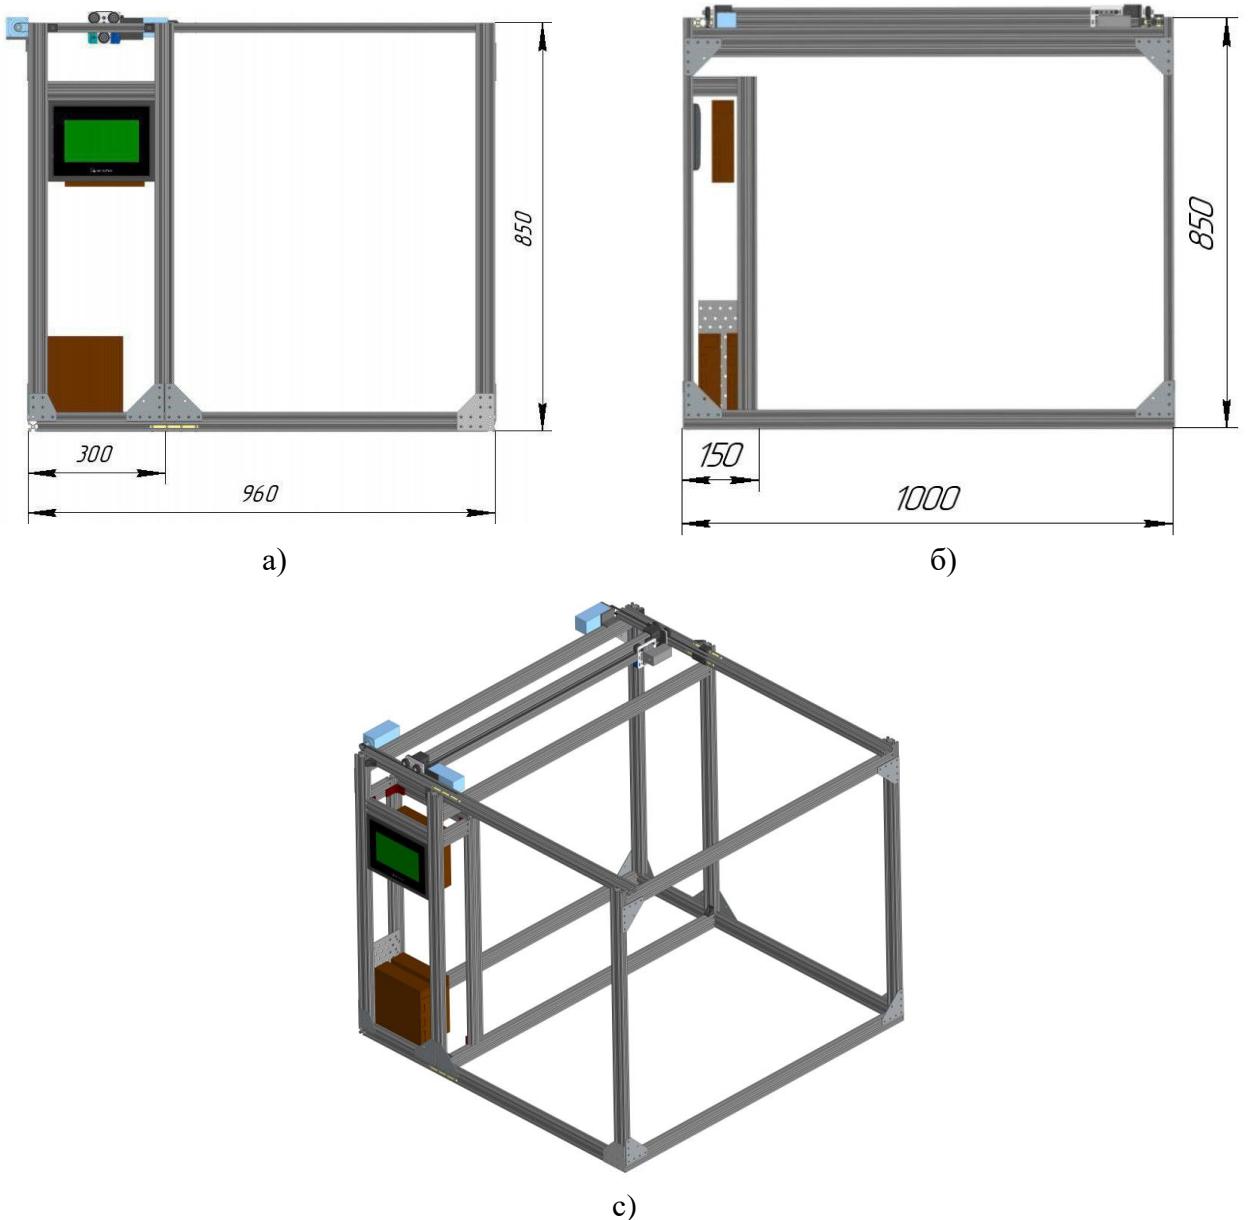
Общий вид макета: а - вид спереди; б - вид сбоку; с - 3D модель
